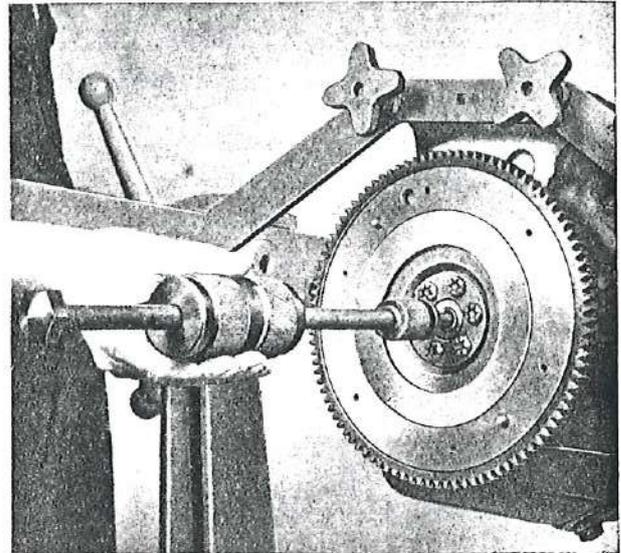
Extracción del casquillo para eje del embrague mediante el extractor a percusión A.6423.
